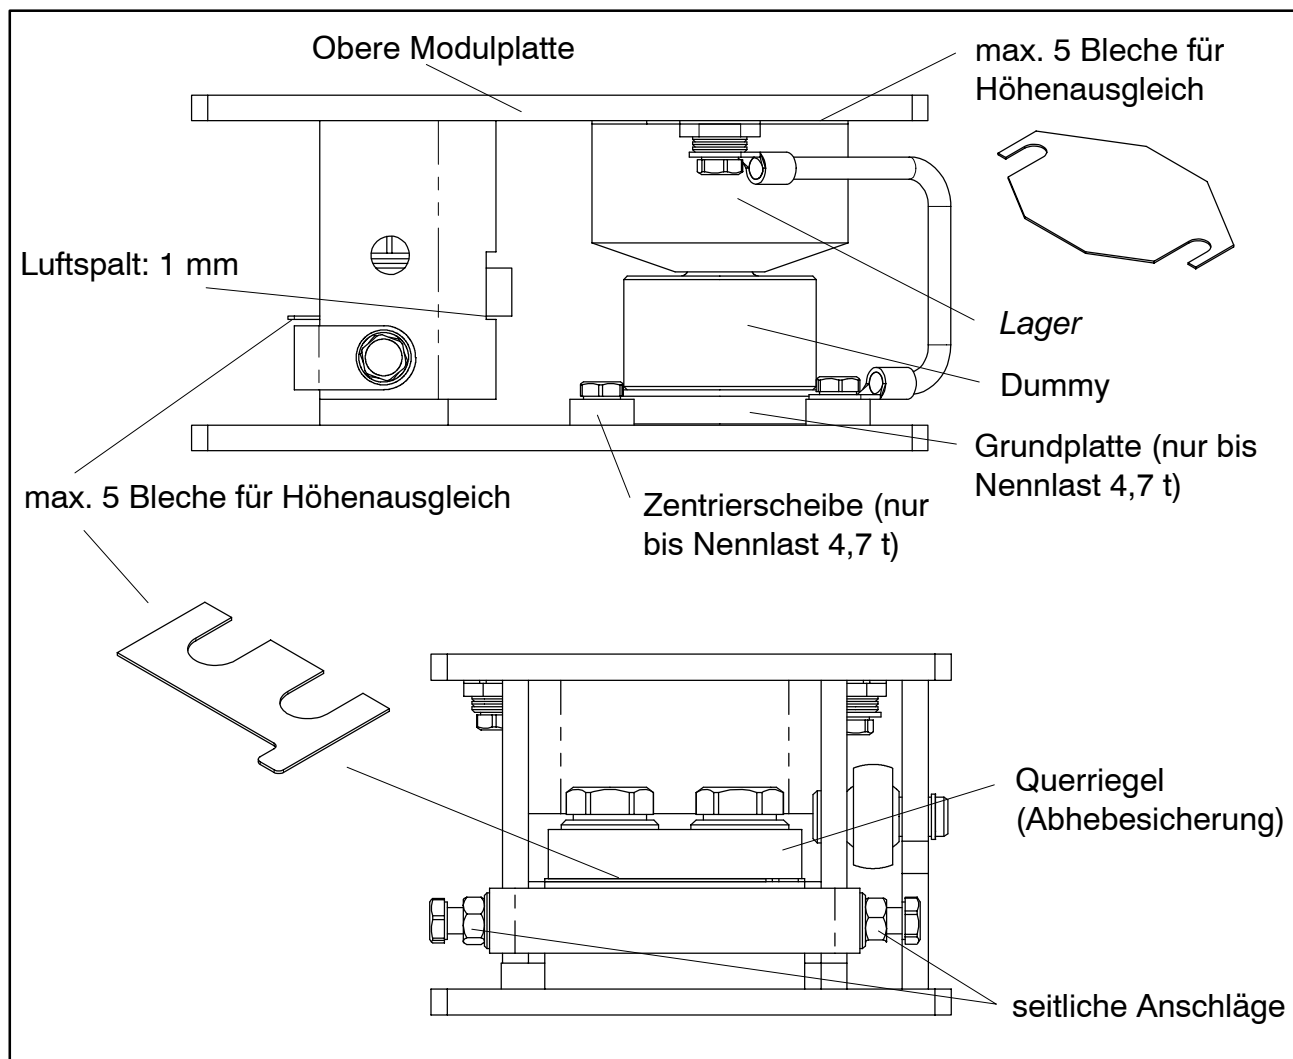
Montage der Ausgleichsbleche bei Ausführung 4,7 t
